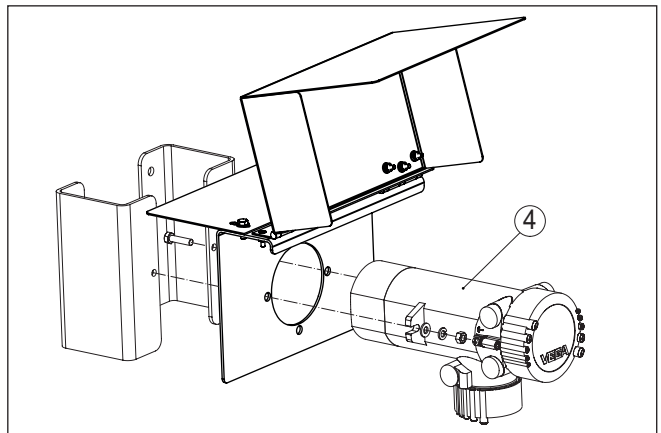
Montage des Sensors (POINTRAC, MINITRAC)
